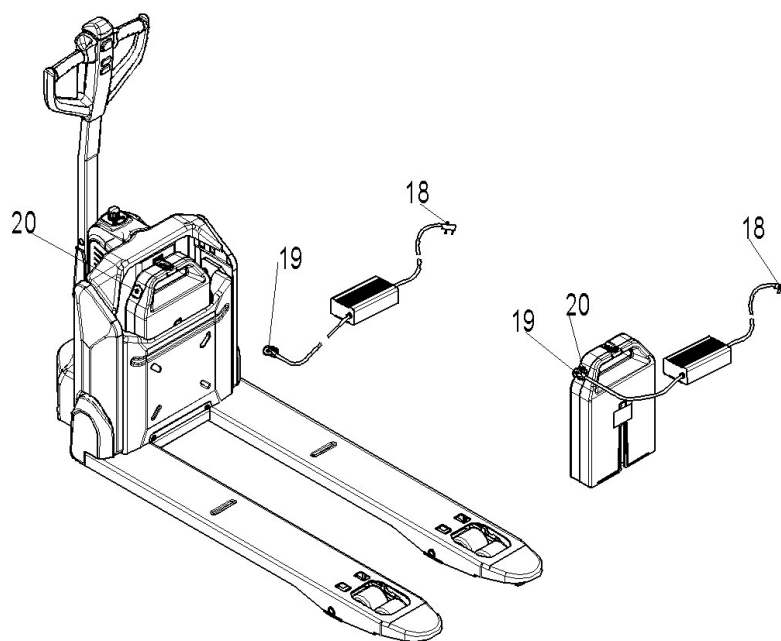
Carga con la batería instalada (izquierda) y con la batería extraída (derecha).
